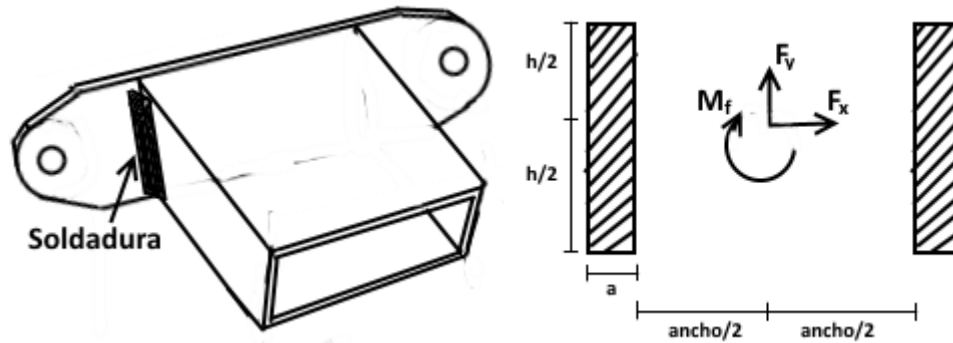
Cordones de soldadura- Tubo transversal
